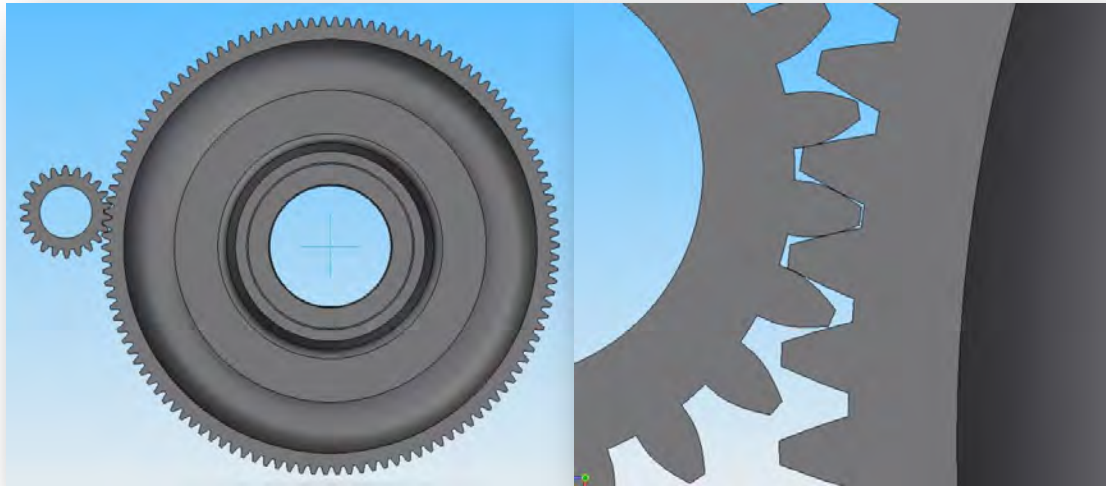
Vista del montaje de la reductora y detalle del punto de engrane.
